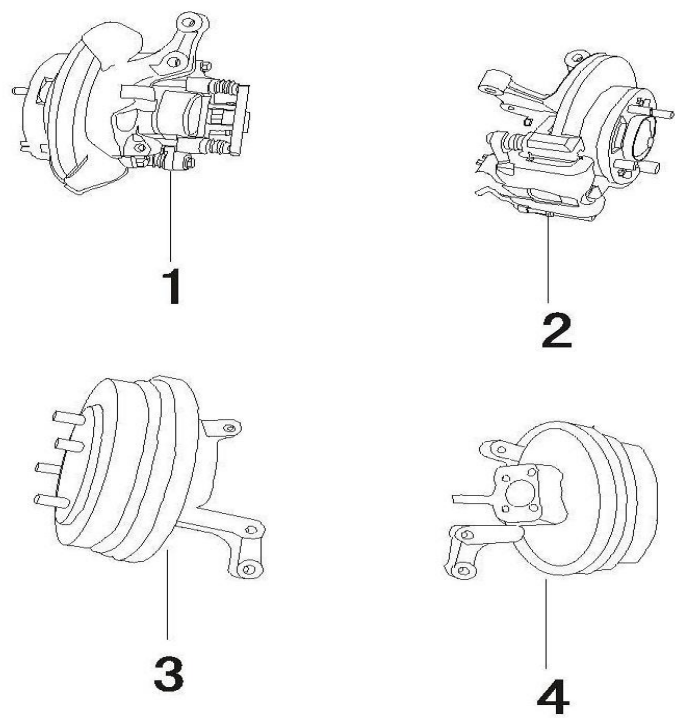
FIG.7		前后制动 FRONT AND REAR BRAKE
